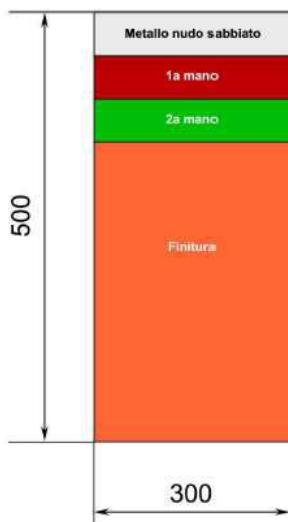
Piastra campione spessore 5 mm – dimensioni in millimetri
